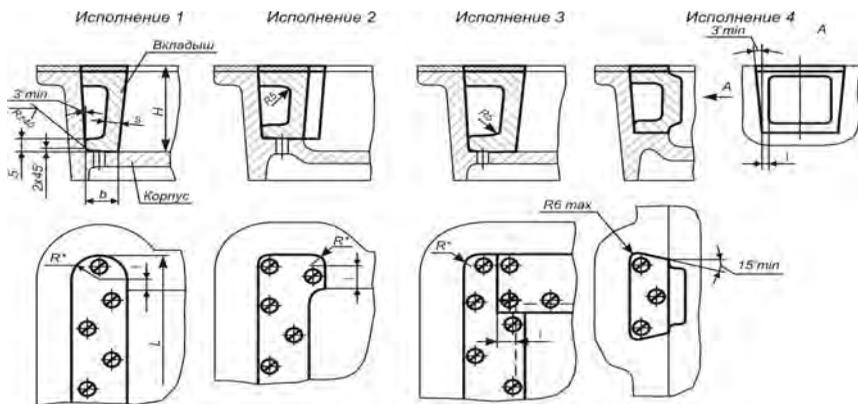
Примеры крепления вкладышей в корпусе стержневого ящика
